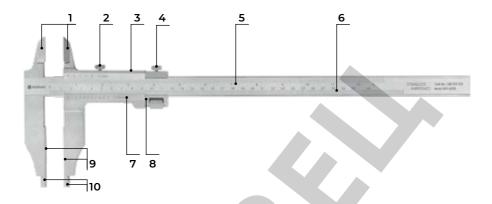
Основные части штангенциркулей модификации двусторонние с глубиномером
